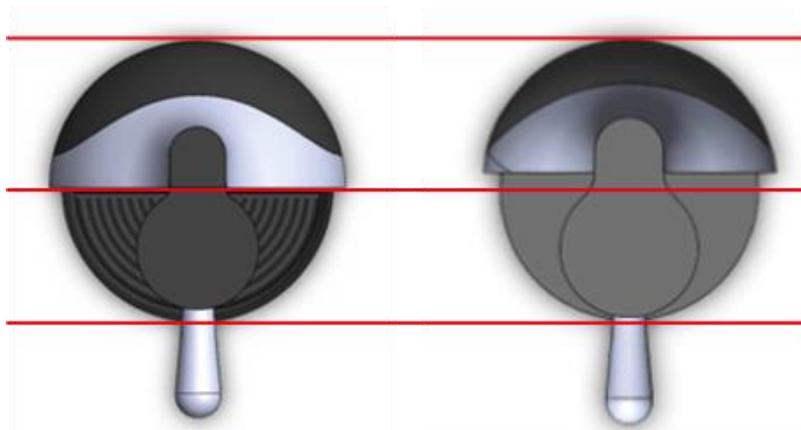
Modelo modificado vs modelo anterior. Vista en planta
